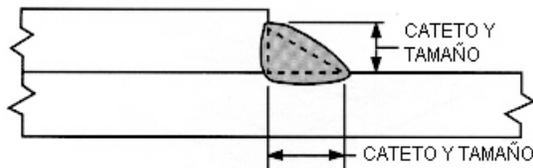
Soldadura de filete con catetos desiguales
